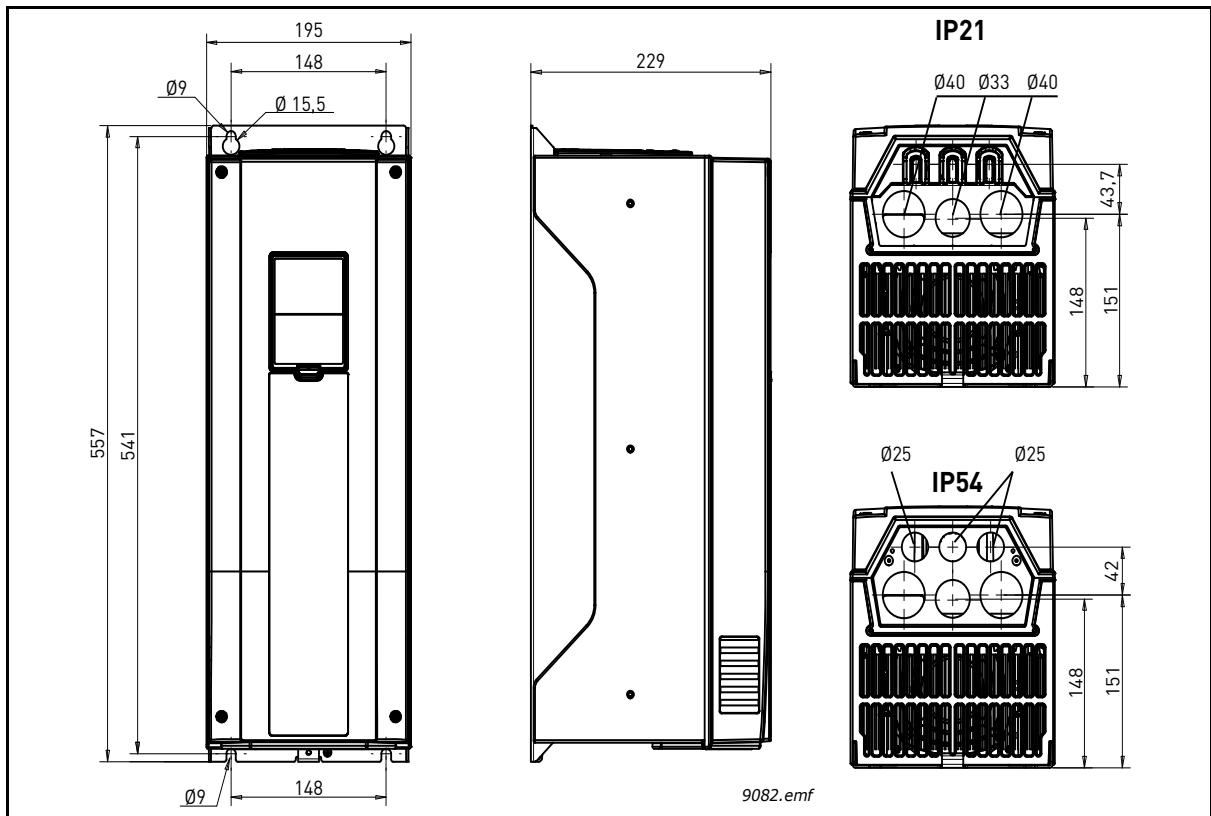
Dimensões do inversor de CA Vacon, MR6, montagem na parede
